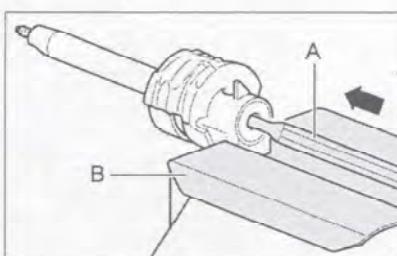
Вытолкните вал из цилиндра с помощью обычного инструмента (A).
